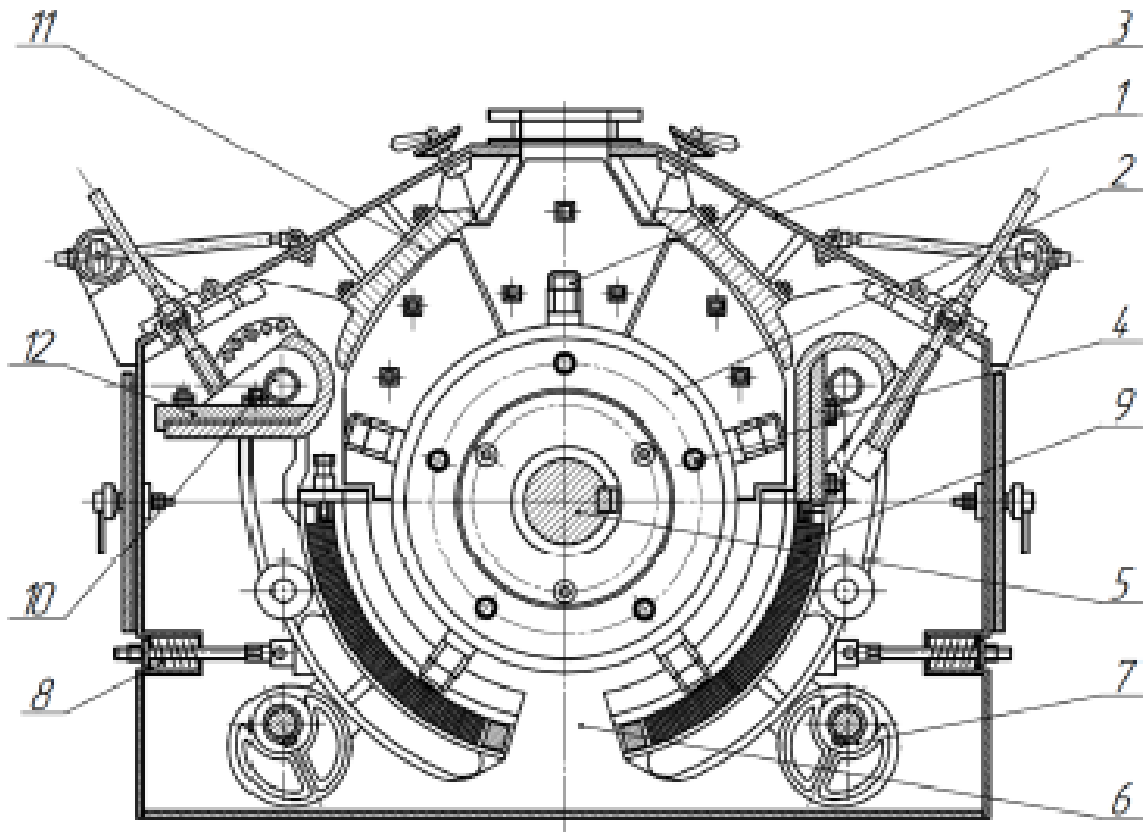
Загальний вид дробарок типу ДМР
